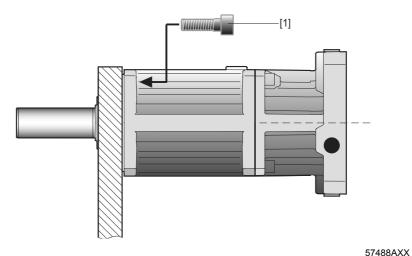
Instalação do servo-redutor planetário PSF... na máquina
